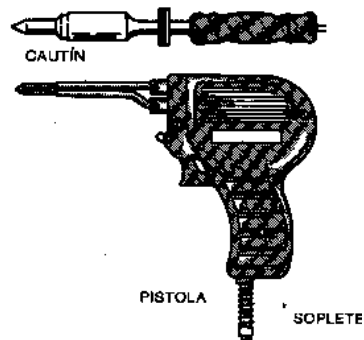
B EQUIPO PARA SOLDADURA
